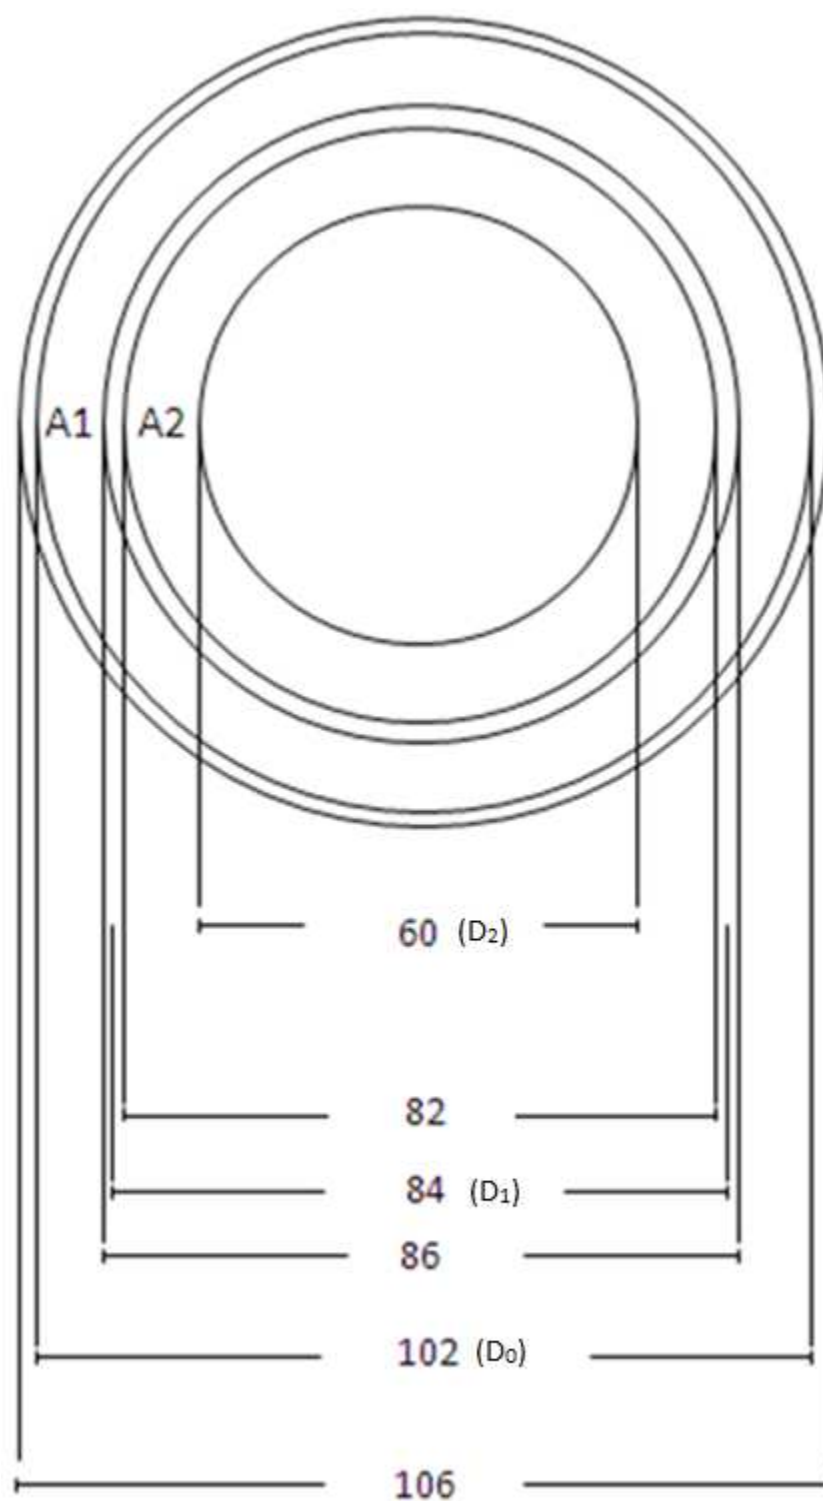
Planta do dispositivo placas coalescentes. Medidas em milímetros. Valores iniciais de projeto.
